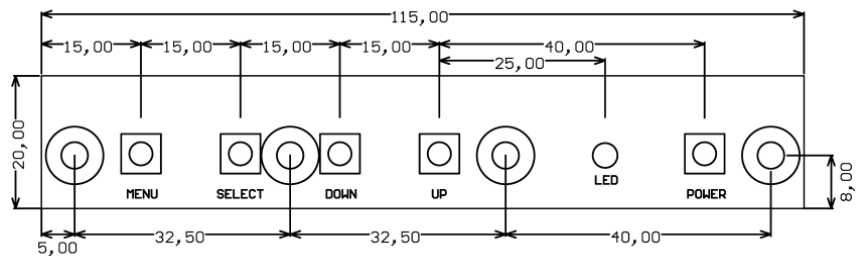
Габаритный чертёж OSD-клавиатуры
